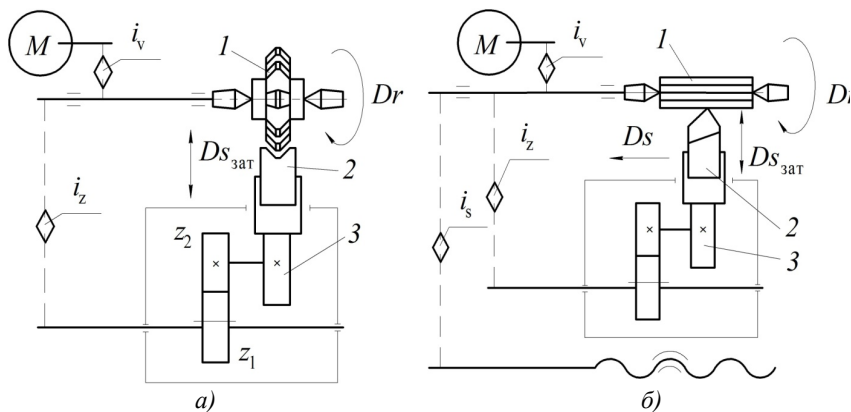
Кинематическая схема затылования дисковой фасонной фрезы (а) и цилиндрической фрезы с прямыми канавками (б): 1 – заготовка; 2 – резец; 3 – кулачок
